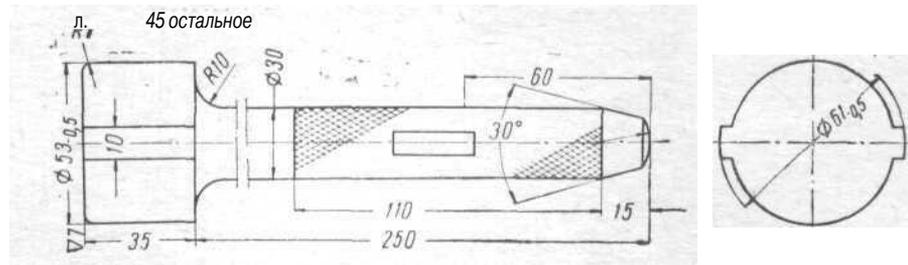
Оправка для выпрессовывания переднего подшипника вала ведущей шестерни главной передачи одновременно с сальником
